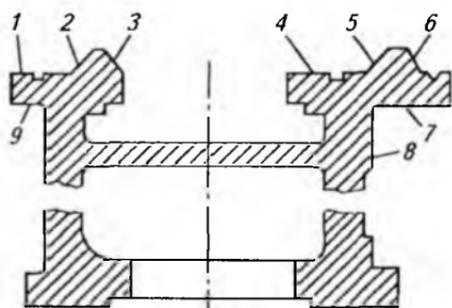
Профиль направляющих станины токарно-винторезного станка 16К20:
